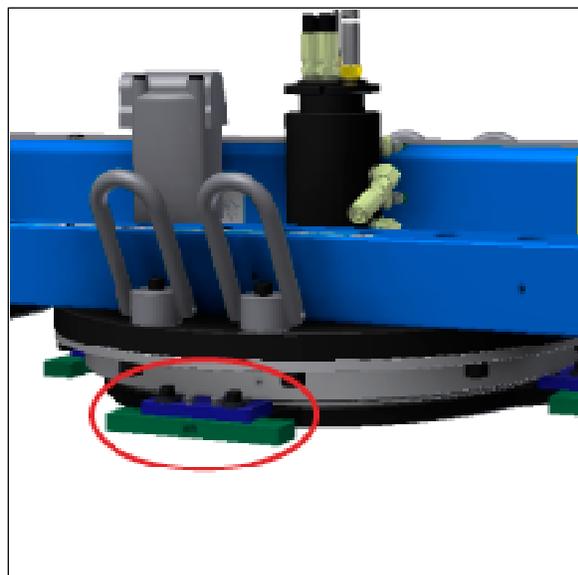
Schweißblöcke an die Grundplattenvergrößerungen anschweißen
